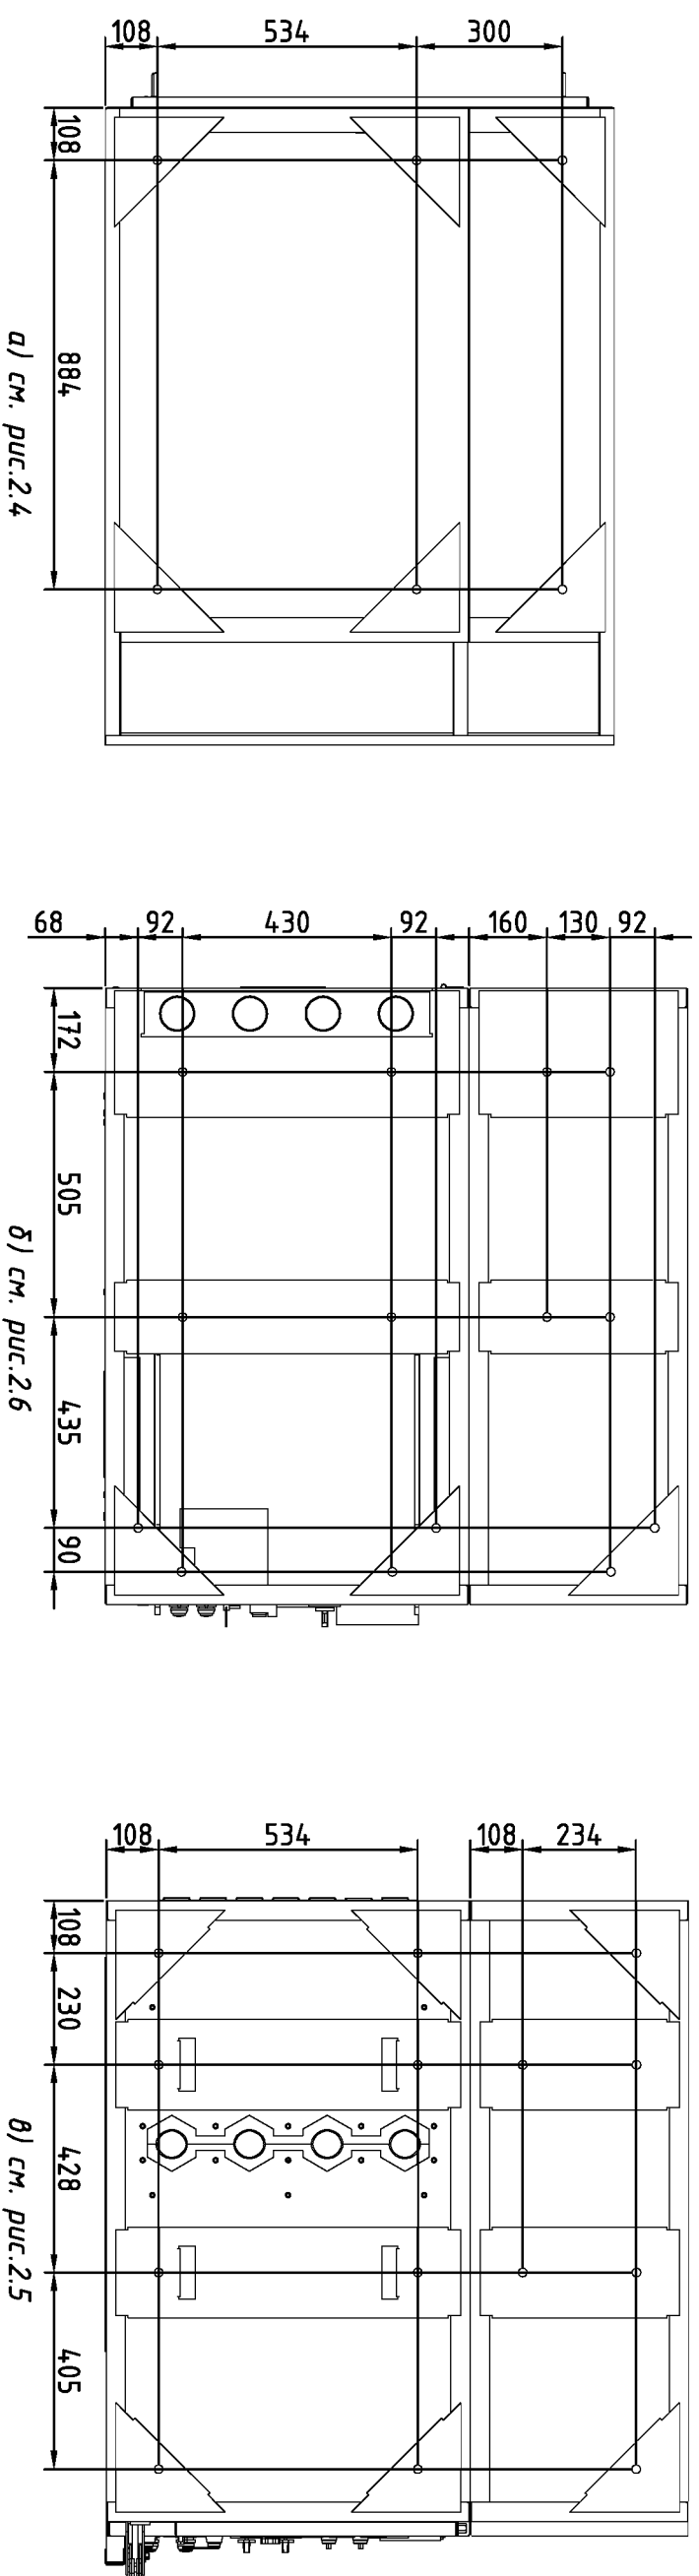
Шкафы ШВВ с выключателем нагрузки и предохранителями
